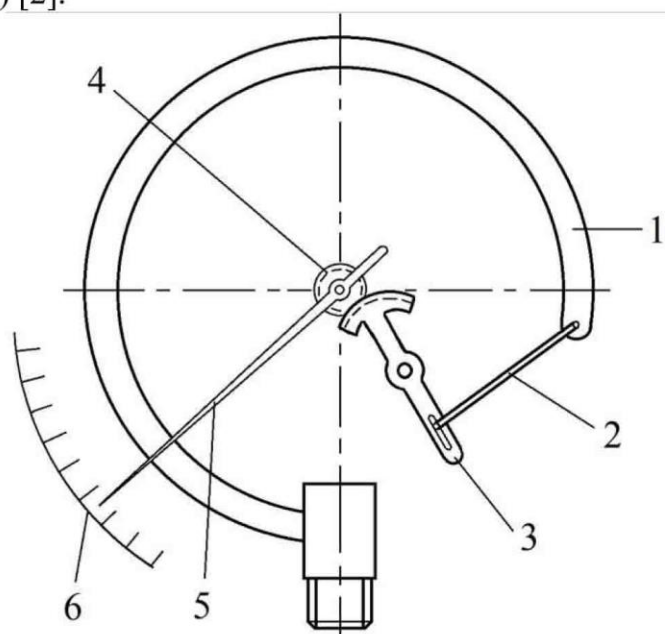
Схема манометра с трубчатой пружиной и передаточным механизмом в виде зубчатого сектора: 1 - трубчатая пружина (трубка Бурдона); 2 – тяга (поводок); 3 - зубчатый сектор; 4 – зубчатое колесо (трибка); 5 – стрелка; 6 - шкала
